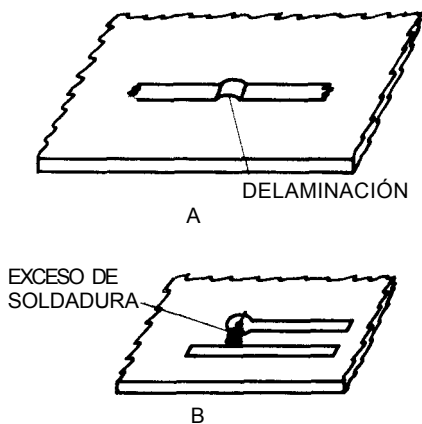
Defectos en el circuito impreso provocados por calentamiento o soldadura excesivos: (A) delaminación o separación del conductor de la superficie de la placa base; (B) el exceso de soldadura puede poner en corto conductores adyacentes.
